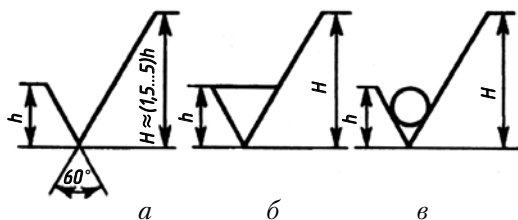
Форма и размеры знаков шероховатости поверхностей
